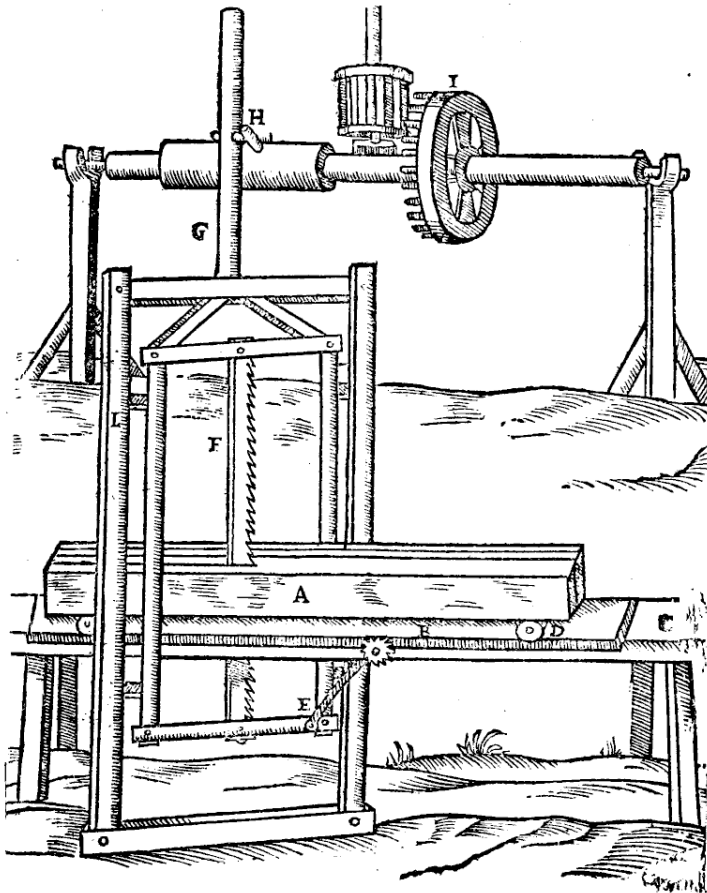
Machine à scier le bois au XVII^e siècle (GIOVANNI BRANCA).
